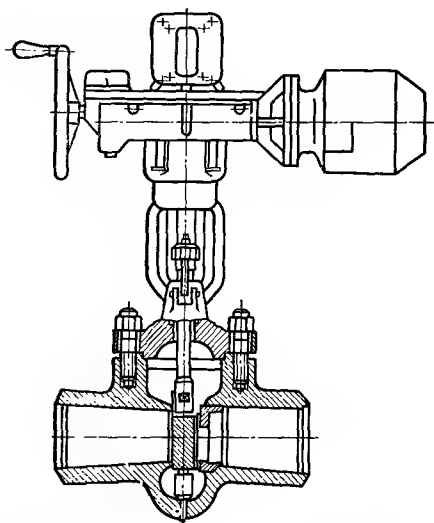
Паровой редукционный (дрессельный) клапан шиберной конструкции
